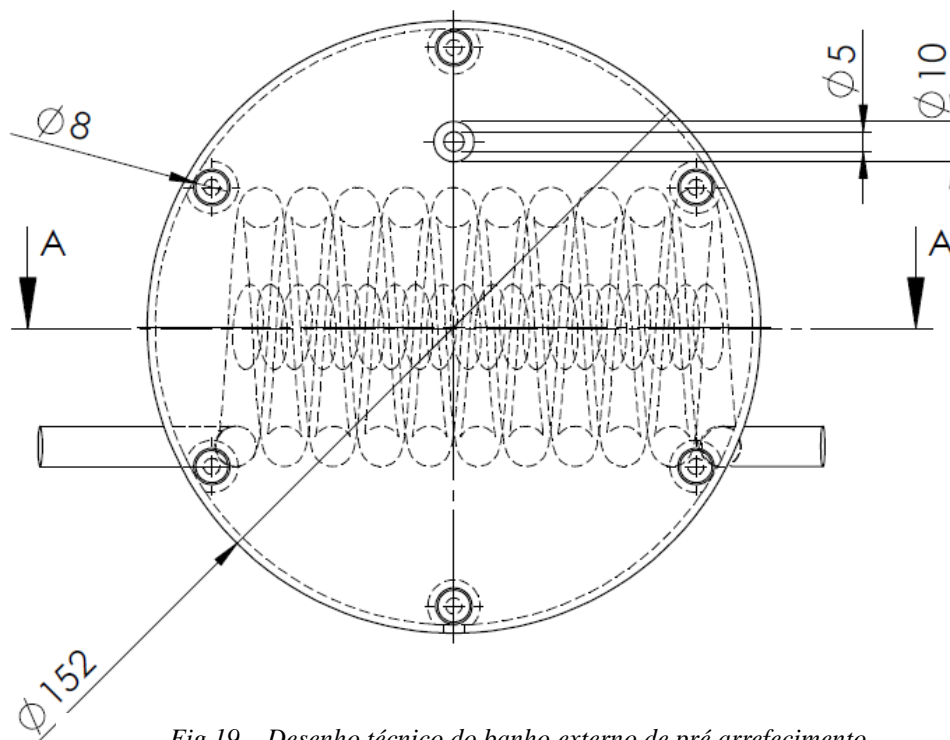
Desenho técnico do banho externo de pré-arrefecimento
